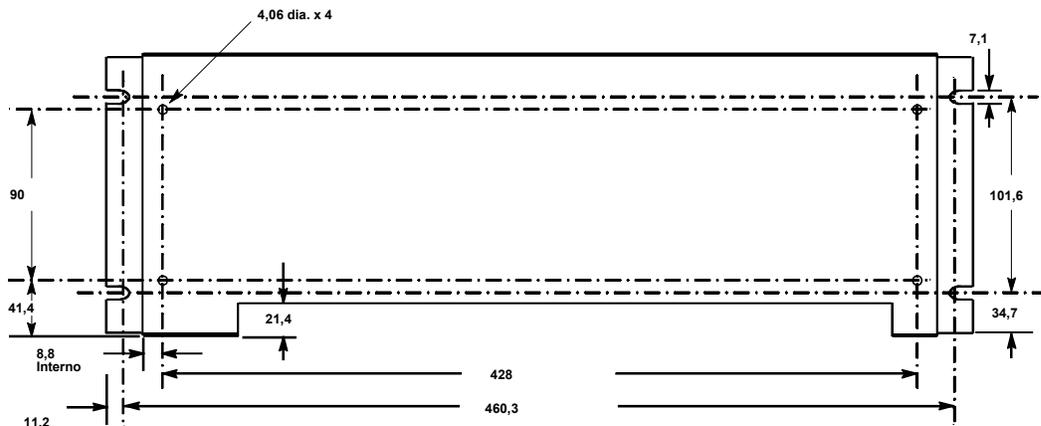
Installazione del sostegno adattatore per il montaggio frontale IC693ACC308
